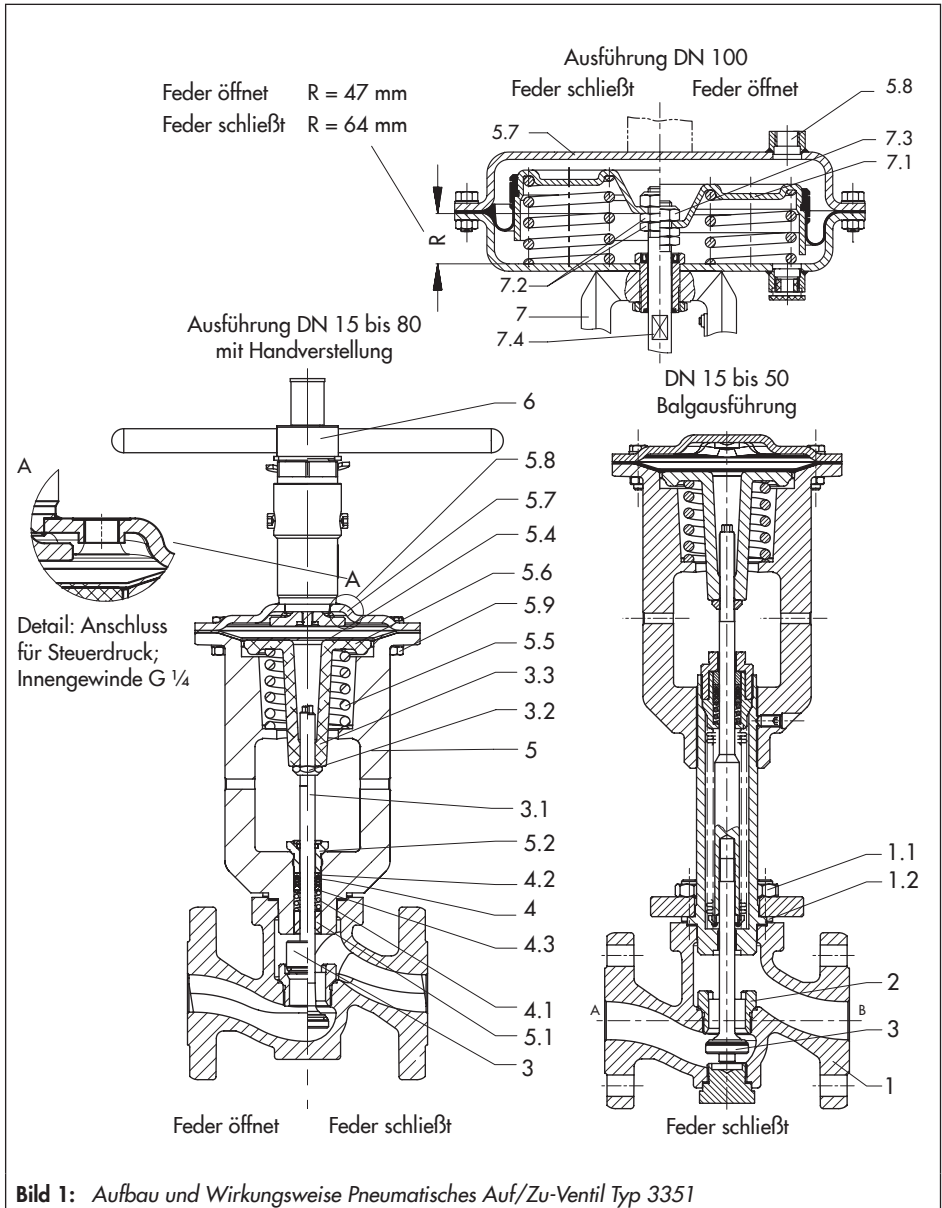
Aufbau und Wirkungsweise Pneumatisches Auf/Zu-Ventil Typ 3351
